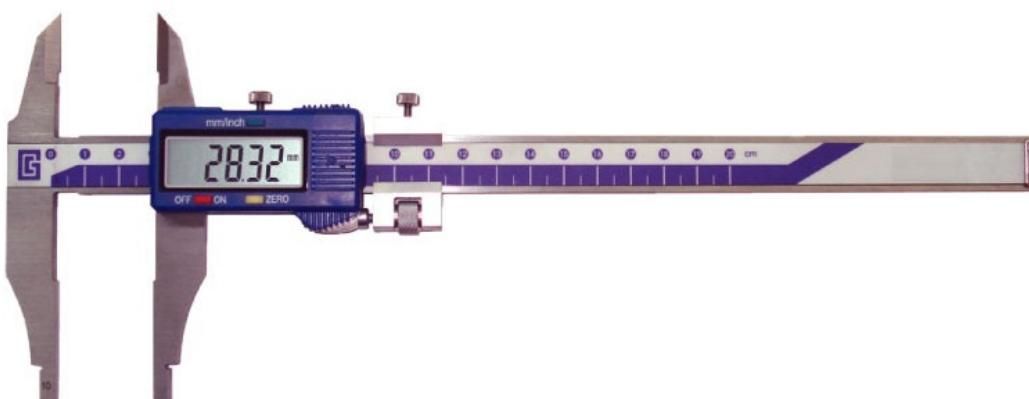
Общий вид штангенциркулей типа ШЦЦ-II.
